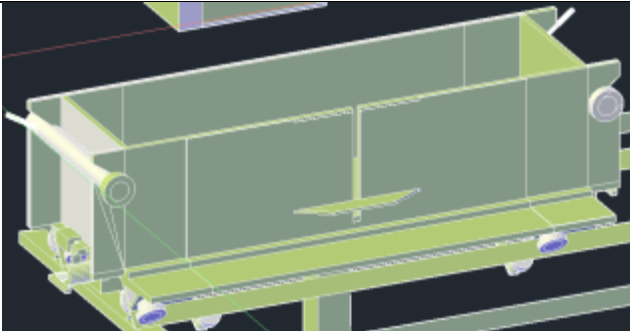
Mesa Compactadora em detalhe (A – roda de aço; B – contra-peso; C – motor; e D - molde de placas
